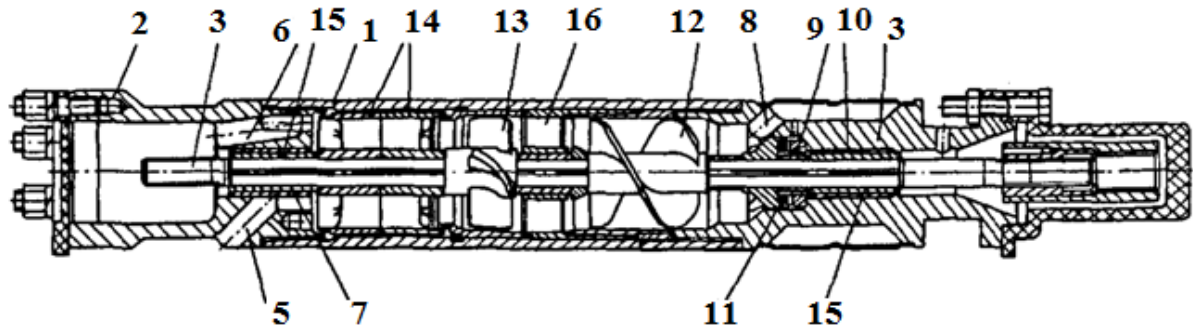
Газосепаратор: 1 – трубный корпус; 2 – головка; 3 – основание; 4 – вал; 5, 6 – перекрестные каналы; 7, 10, 15 – втулки радиальных подшипников; 8 – полость с каналами; 9 – подпятник; 11 – пята; 12 – шнек; 13 – рабочее колесо; 14 - сепараторы.
